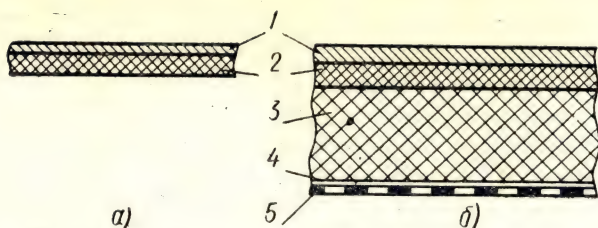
Схемы конструкций стенок кожухов: *а* — для небольших кожухов; *б* — для больших кожухов:
